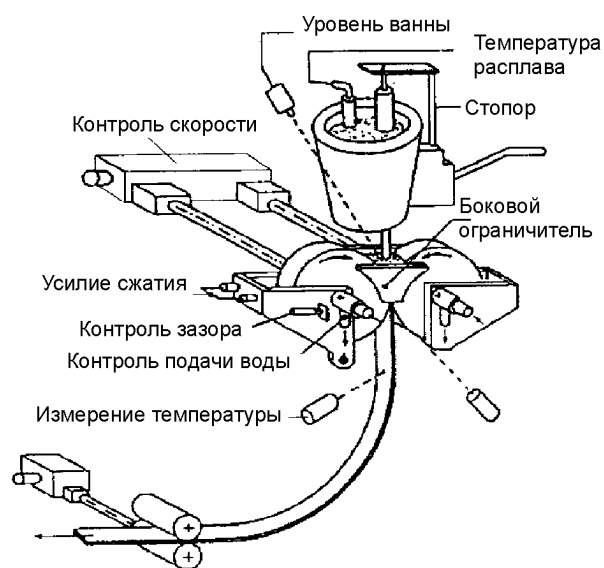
Общий вид установки непрерывного литья тонкой полосы
